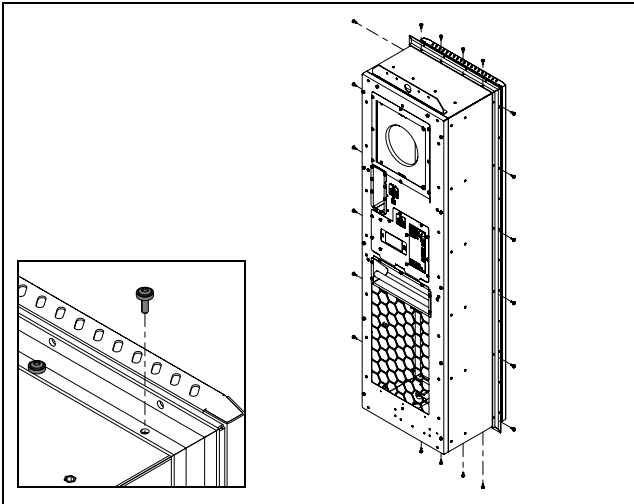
Befestigen des Montagerahmens am Kühlgerät
